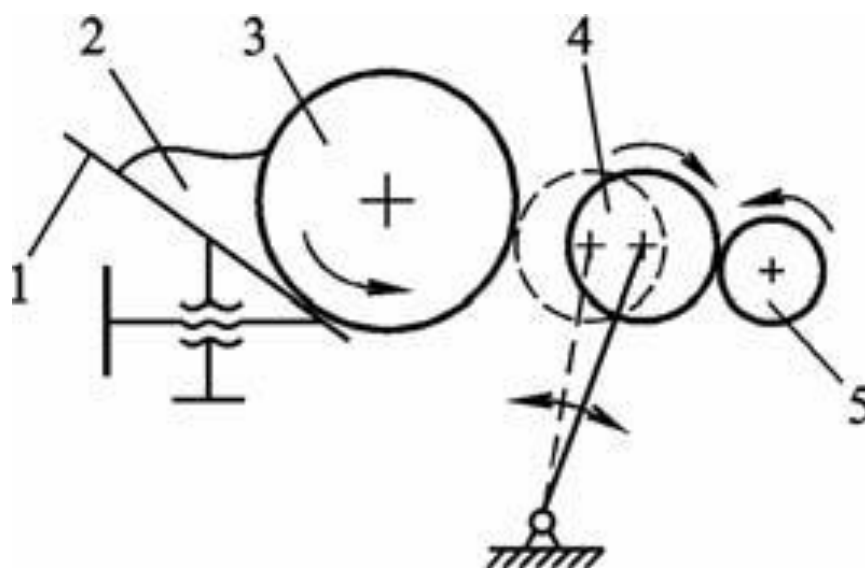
Технологічна схема фарбоподаючої групи фарбового апарату: 1 – барвистий ніж; 2 – фарба; 3 – дукторний вал; 4 – передавальний вал; 5 – циліндр розкочуючої групи
